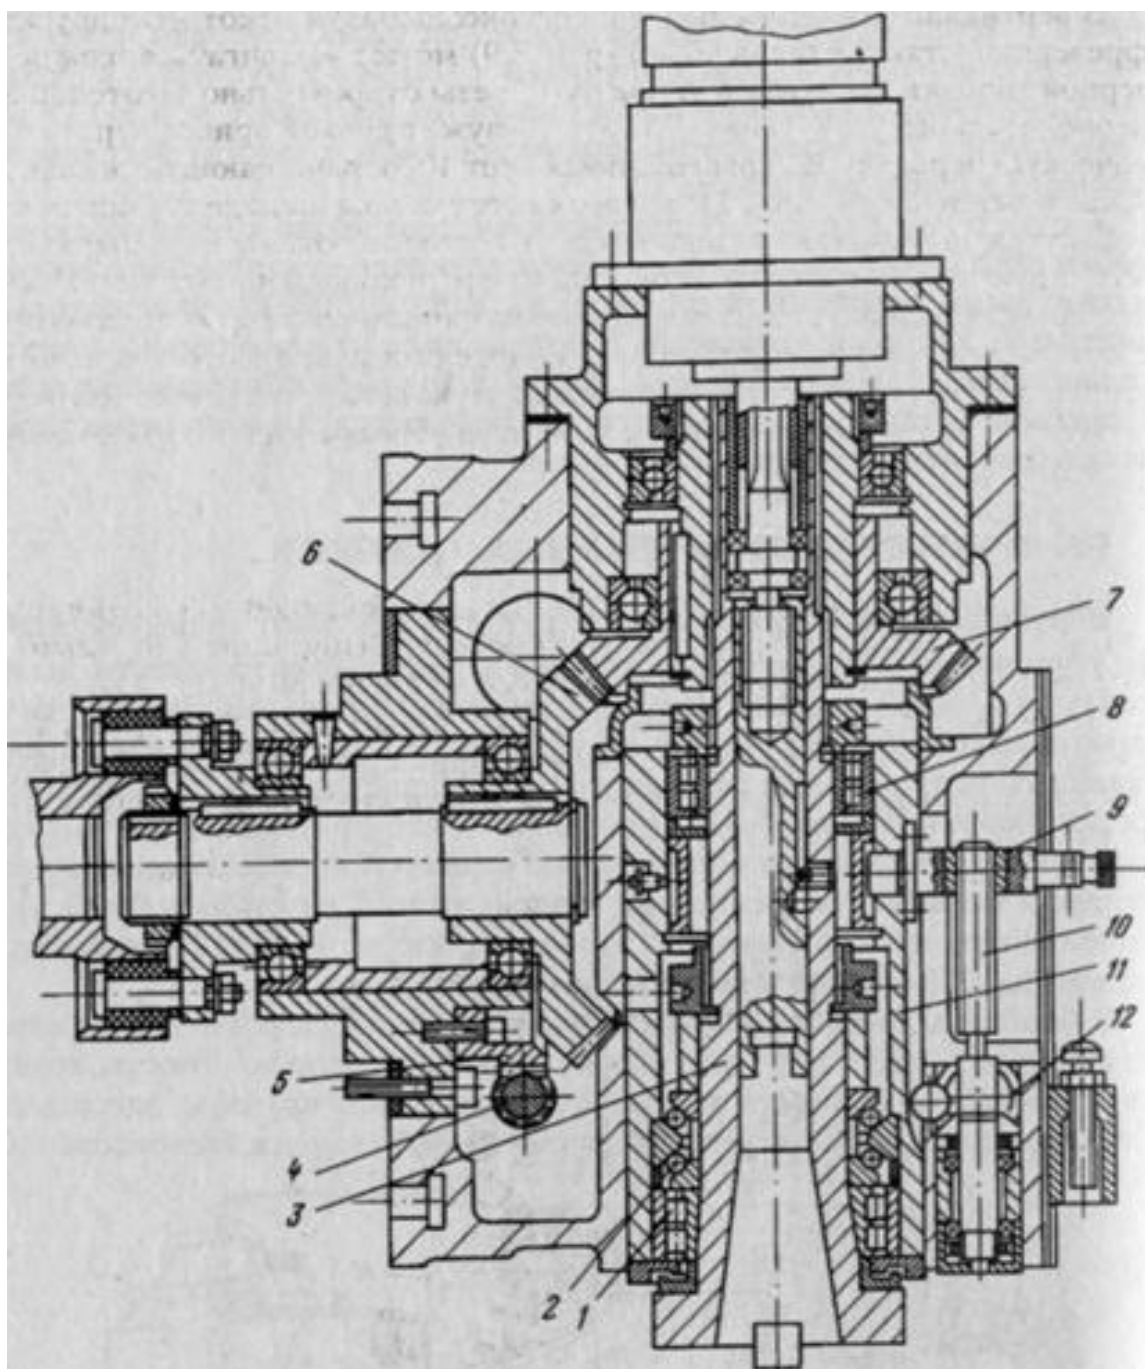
Фрезерная головка вертикального консольного фрезерного станка.
